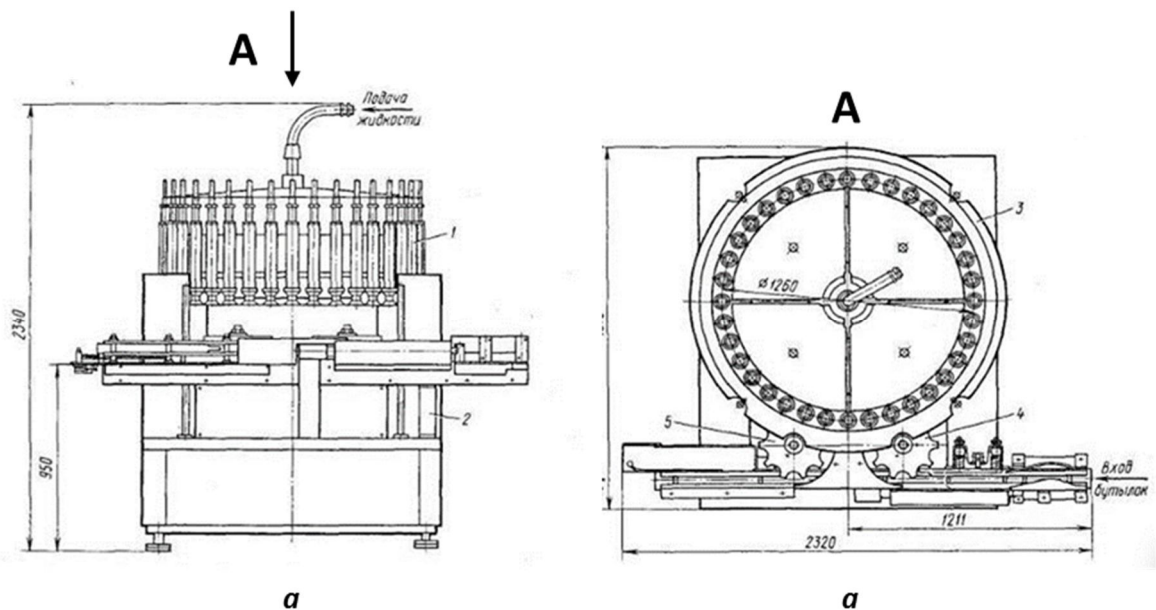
Фасувальна машина Т1-ВНА-12: а – вид фронтальний; б – вид зверху: 1 - фасувальний пристрій; 2 - станина; 3 - карусель; 4 - механізм завантаження пляшок; 5 - механізм розвантаження пляшок
